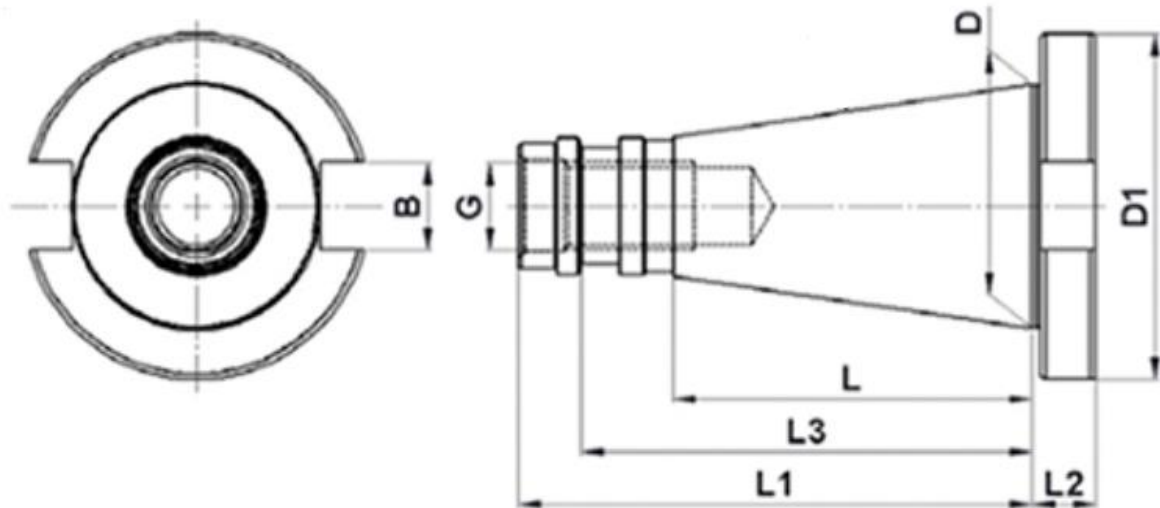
Vista frontal e lateral de um cone ISSO [53].
